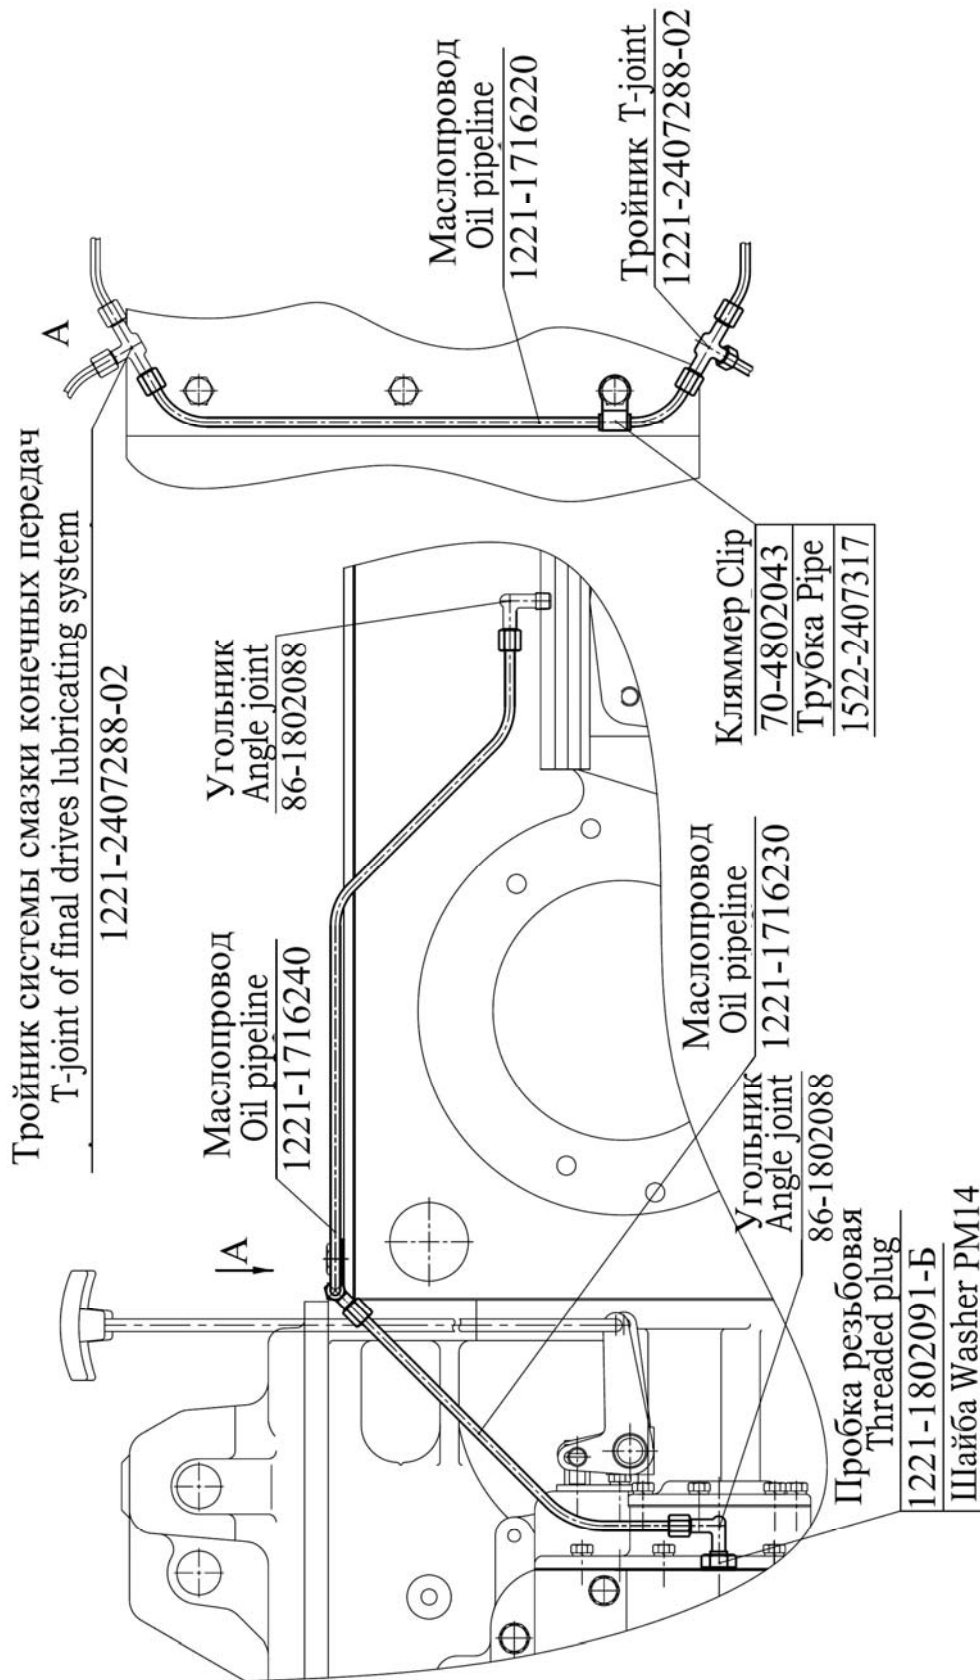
Схема смазки ходоуменьшителя тракторов Беларус-1221/1523.
